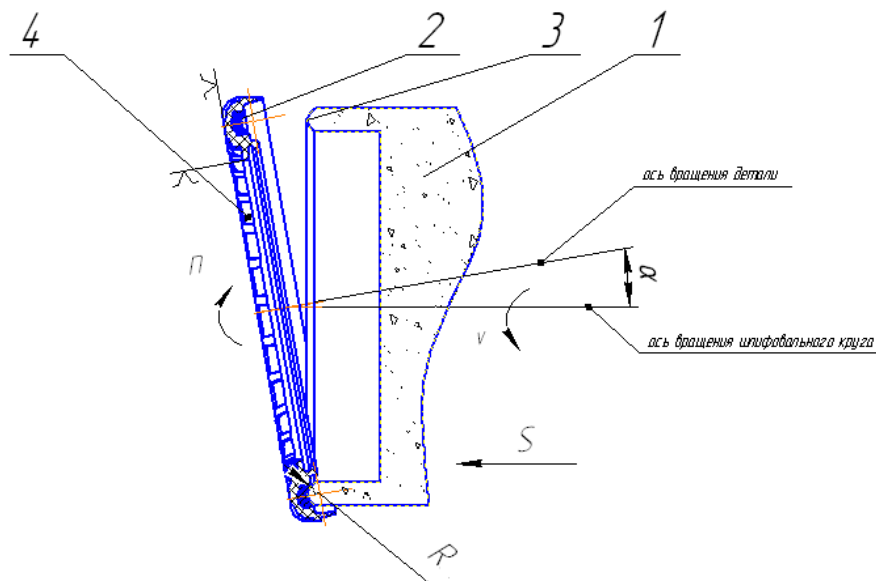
Схема шлифования дорожек качения упорных подшипников способом торцевого шлифования
